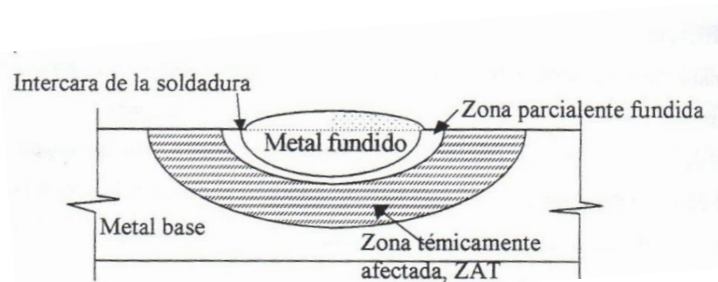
Zonas metalúrgicas producidas en una junta soldada.
